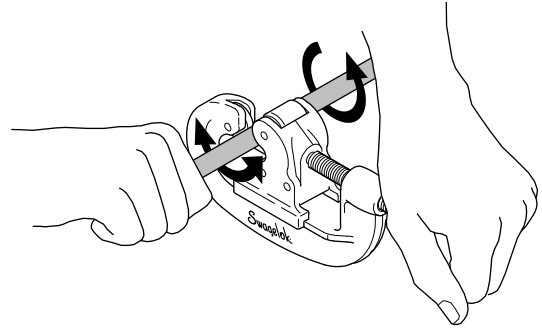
Gire la cortadora de tubos completamente alrededor del tubo
